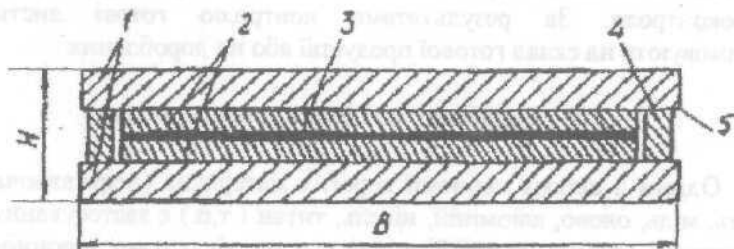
Складений симетричний пакет: 1 - основний шар; 2 - плакуючий шар; 3 - шар ізоляції; 4 - прокладки; 5 -сварной шов
